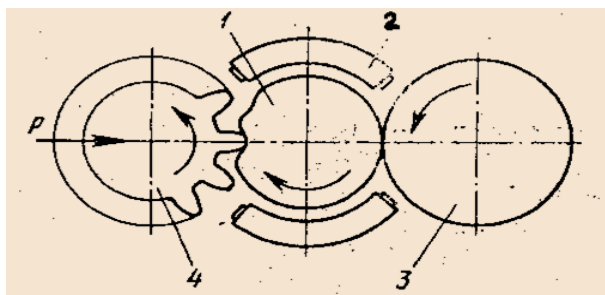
Схема горячей накатки зубьев зубчатого колеса
